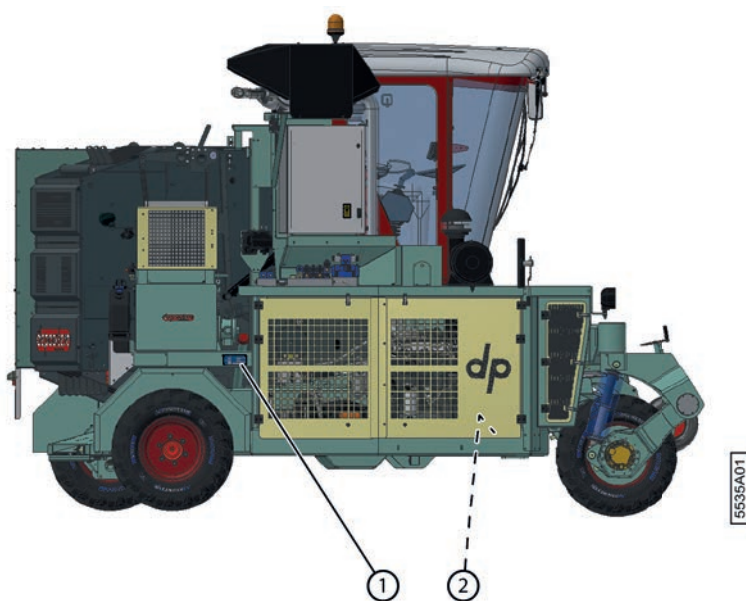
Emplacement de la plaque d'identification et du numéro de châssis sur la machine
